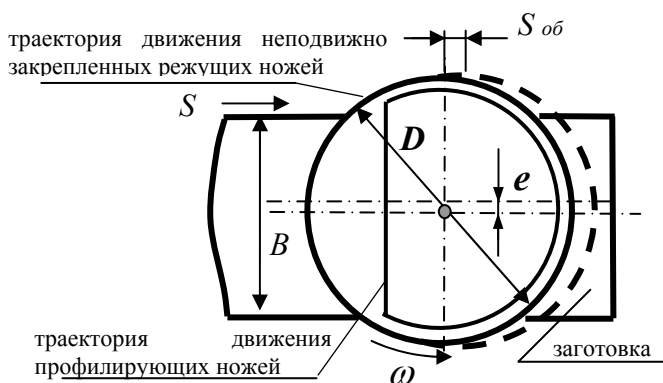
Предложенные траектории движения режущих ножей торцово фрезы относительно заготовки
